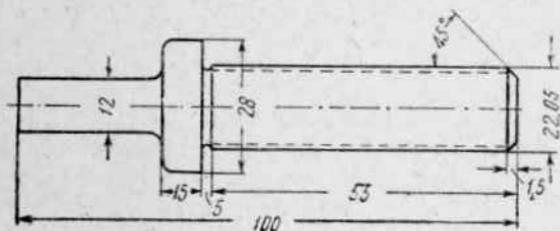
Резьбовая фреза для фрезерования плашек.
